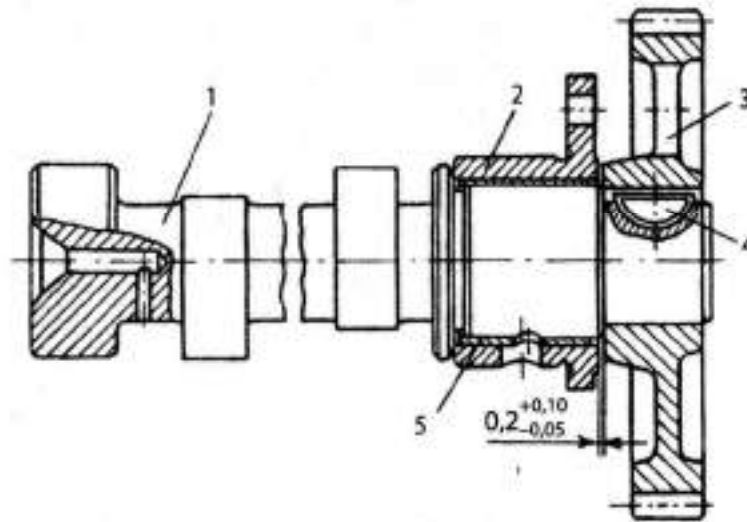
Установлення зазору між шестірнею і вальницею розподільного вала
